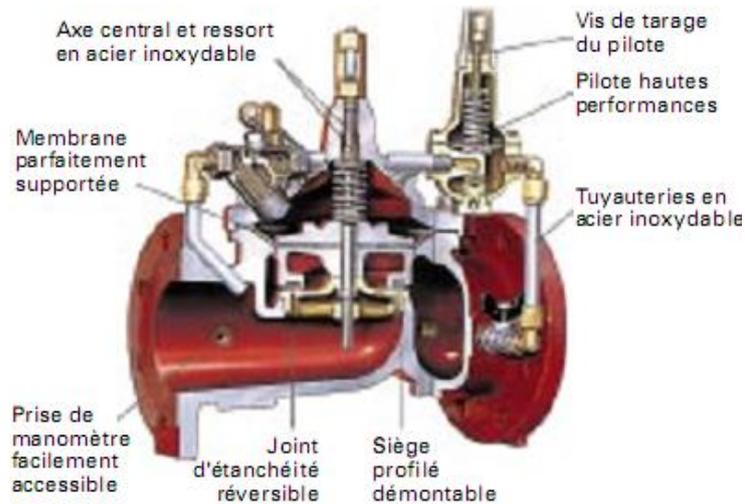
réducteur de pression modulaire (d’après document Pont-à-Mousson)
